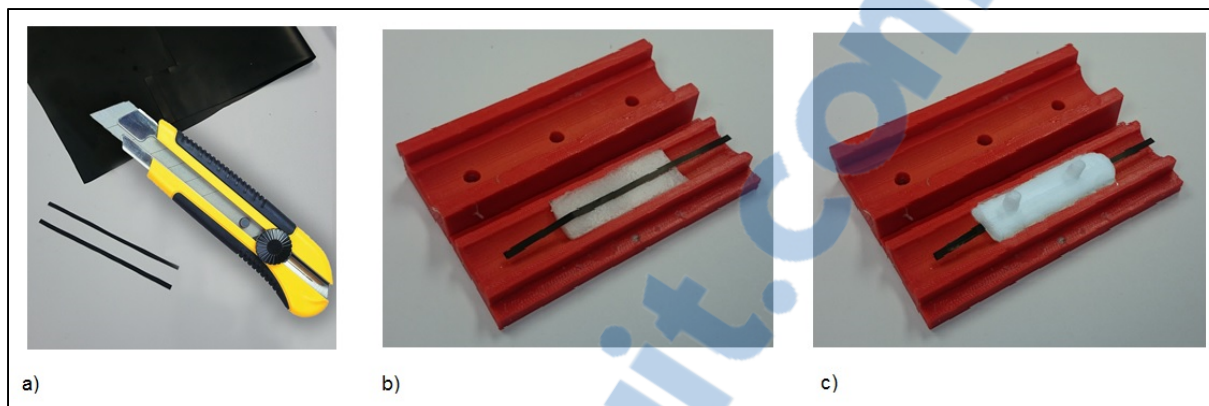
(a) Découpe des filaments de polymère (b) Insertion du filament au centre de la mousse de silicone (c) Moulage final du SMEI
